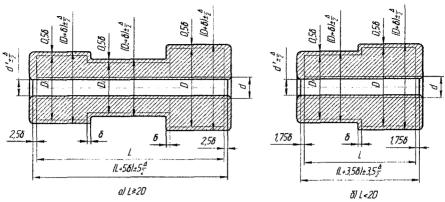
Схема назначения припусков и допусков для поковок 5-ой группы
